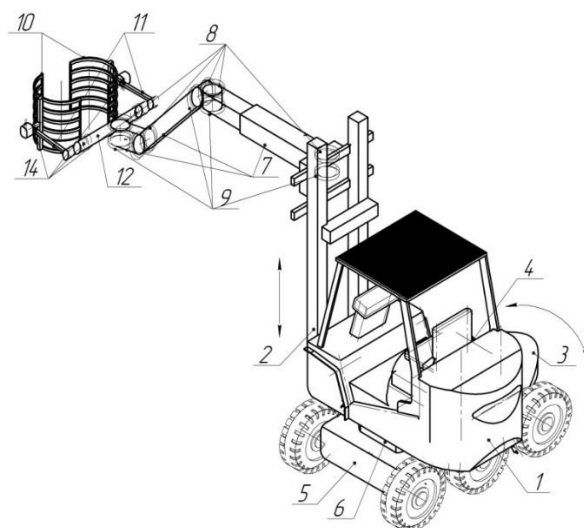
Общий вид погрузочно-транспортного агрегата:
